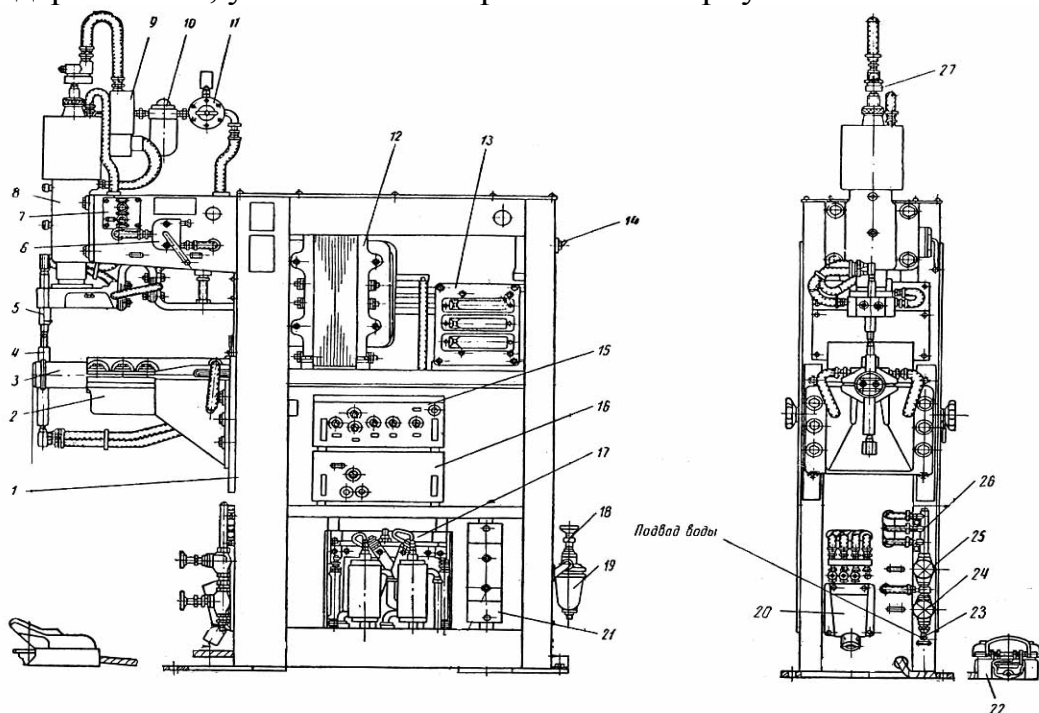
Общий вид машины для точечной контактной сварки МТ-1613
